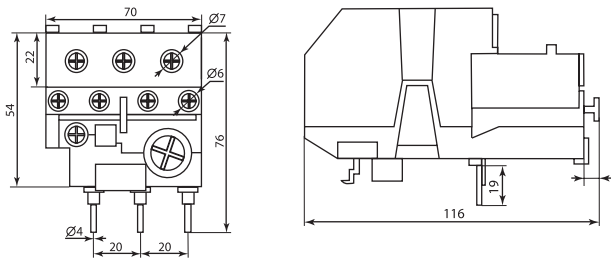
Габаритные и установочные размеры реле РТЛУ-2053-М2...РТЛУ-2066-М2
